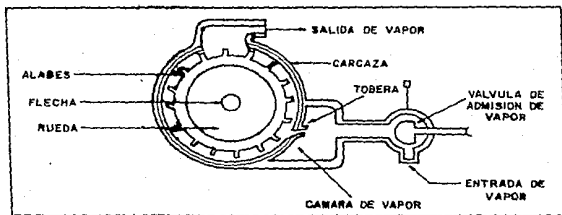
PARTES QUE INTEGRAN LA TURBINA
